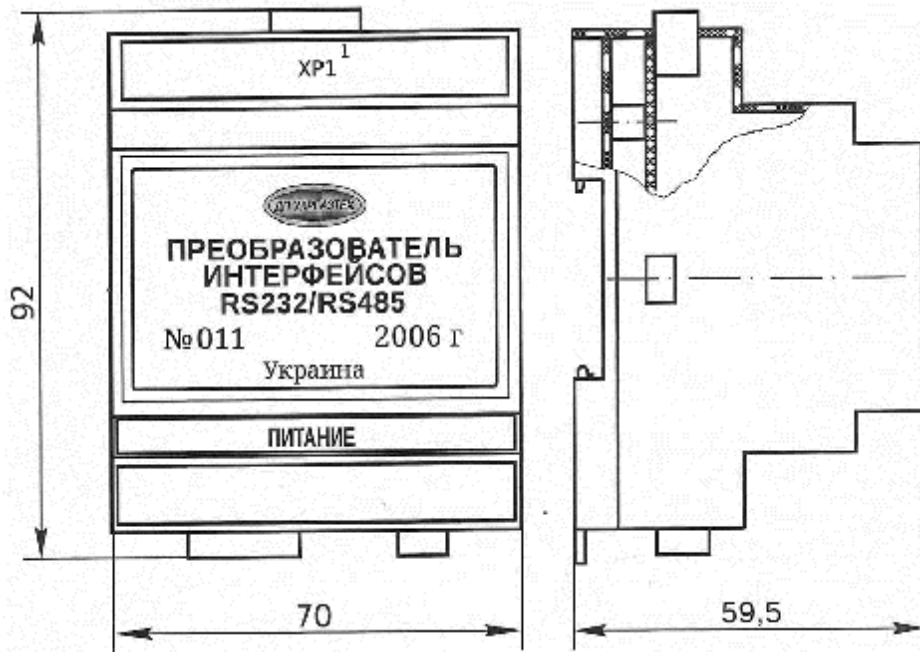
Преобразователь исполнения –03. Корпус в виде конструкции для установки на DIN-рейке
